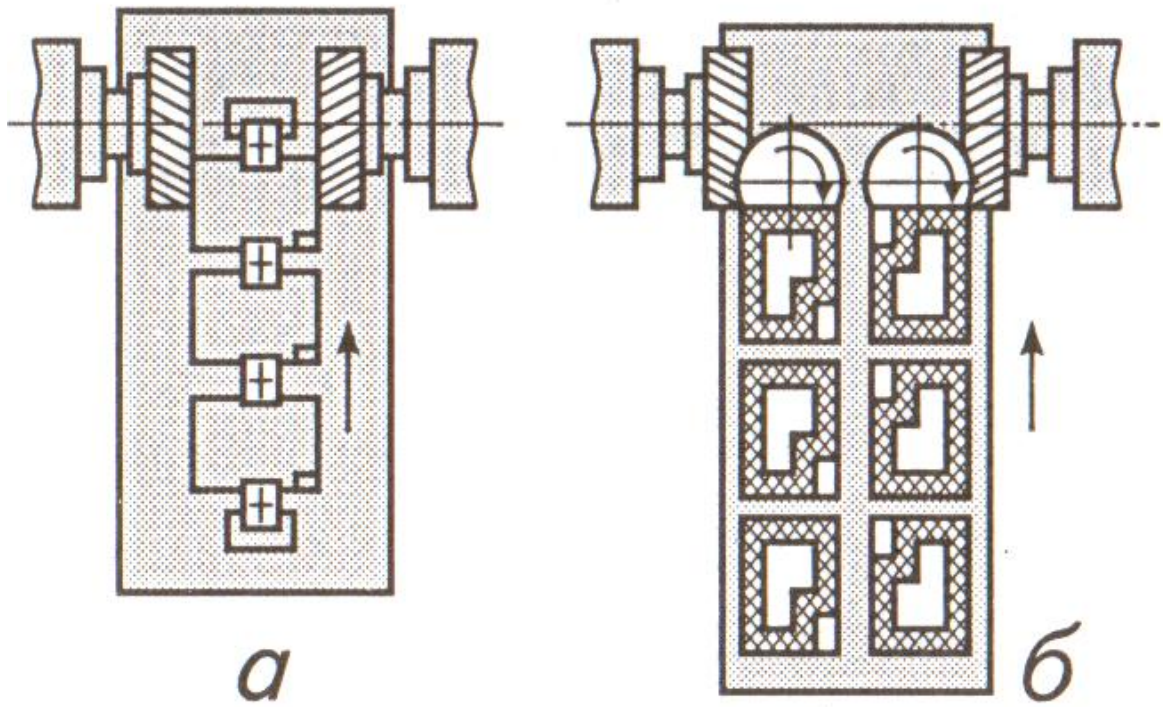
Групове фрезерування двома торцевими фрезами
